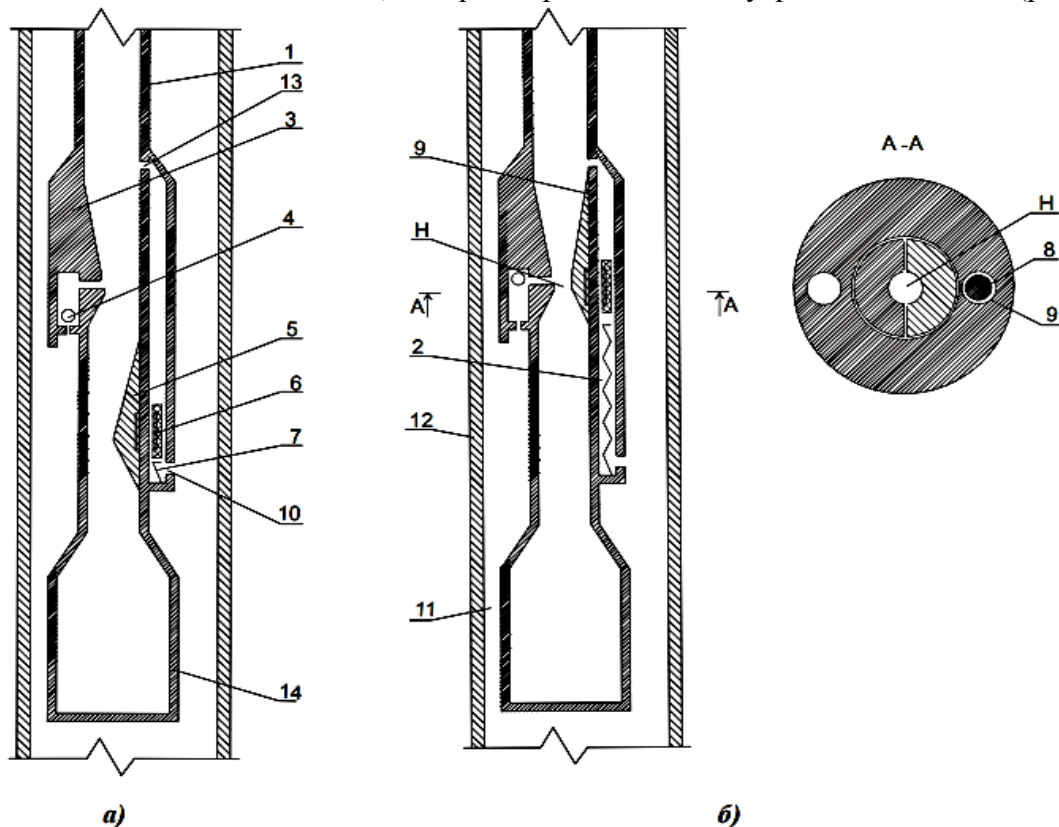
Струйный аппарат для перепуска затрубного газа: 1 - колонна НКТ; 2 - подпоршневая полость; 3 - неподвижная симметричная половина; 4 - обратный клапан; 5- подвижная симметричная половина; 6- магнит; 7 - пружина; 8 - поршень; 9 - цилиндр; 10, 12 - отверстие; 11 - затрубное пространство; 12 - обсадная колонна; 14 - УЭЦН; Н - сужение; а) неактивное положение; б) активное положение (<https://clck.ru/TgMJL>)
